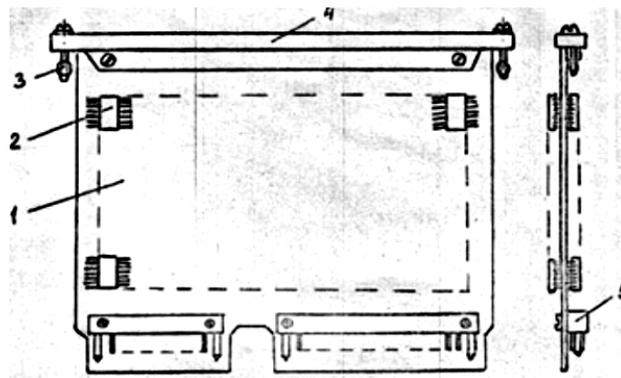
Конструкция бескорпусной ФЯ двухстороннего типа:
